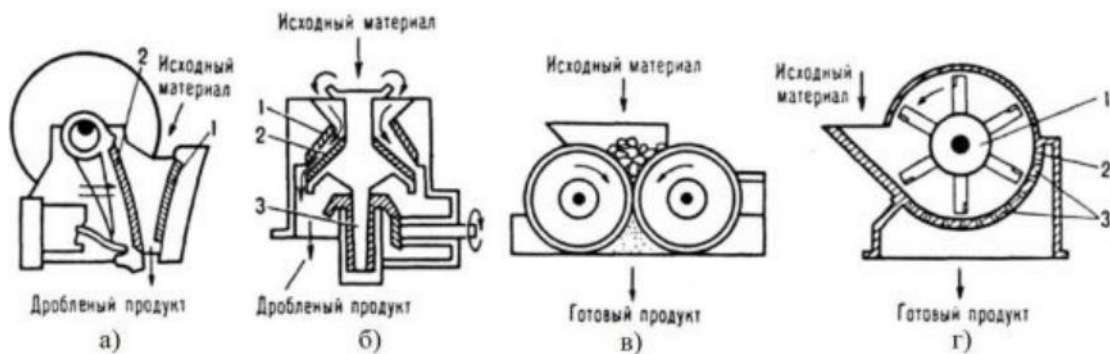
Дробилка: а - щековая (1, 2 - соотв. неподвижная и подвижная щеки); б - конусная (1, 2 - соотв. неподвижный и качающийся конусы, 3 - вал); в - вальцовая; г - роторная или молотковая (1 - ротор с молотками, билами, рифлями и др., 2 - статор, 3 - решето)
